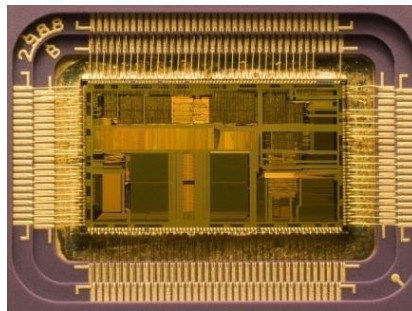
Conexões *wirebonding* em um *chip* de alta densidade para montagem SMD (*Surface Mounting Device*) –Fonte: www.advotech.com
